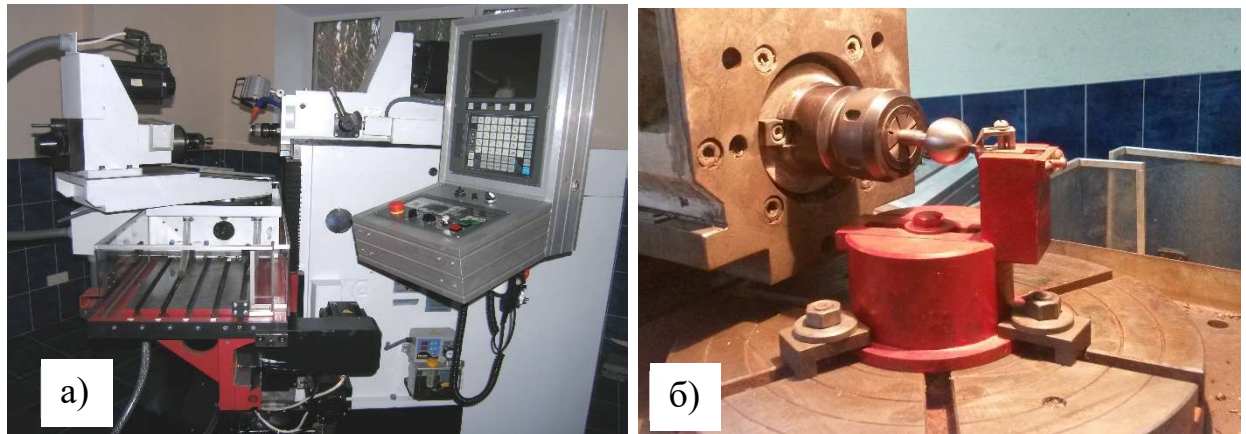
Верстат для точіння сфери : а) загальний вигляд; б) куля з пристроєм для обробки
